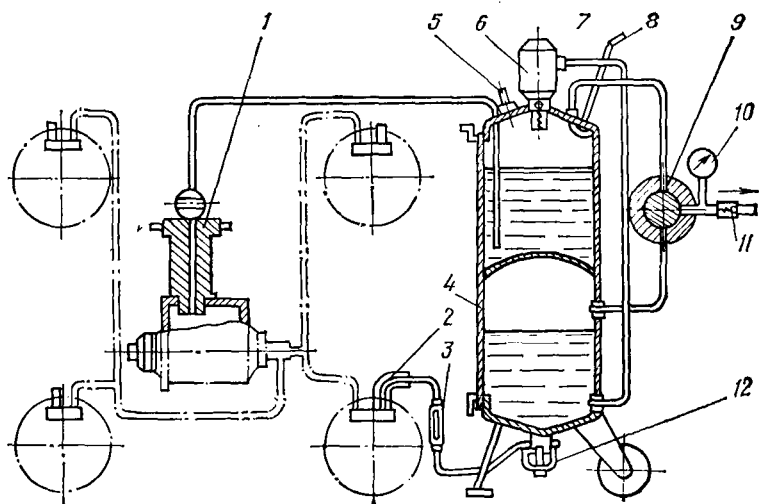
Схема приспособления для прокачки системы гидропривода тормозов автомобилей. Модель 107М:
